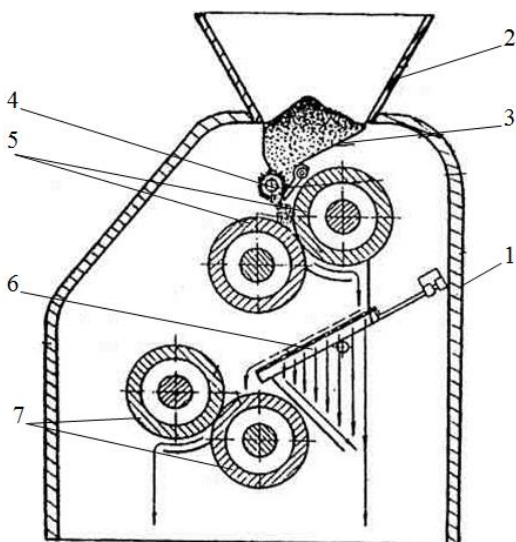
Двопарна чотиривальцьова дробарка: 1 – корпус; 2 – бункер; 3 – розподільний жолоб; 4 – живильний валик; 5 – верхня пара валків; 6 – вібросито; 7 – нижня пара валків.
